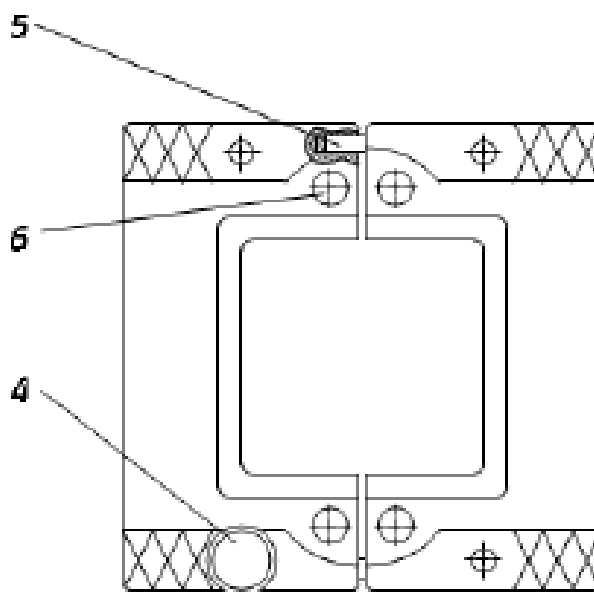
Общий вид крепежной рамки: 4 – шарнирное соединение; 5-
